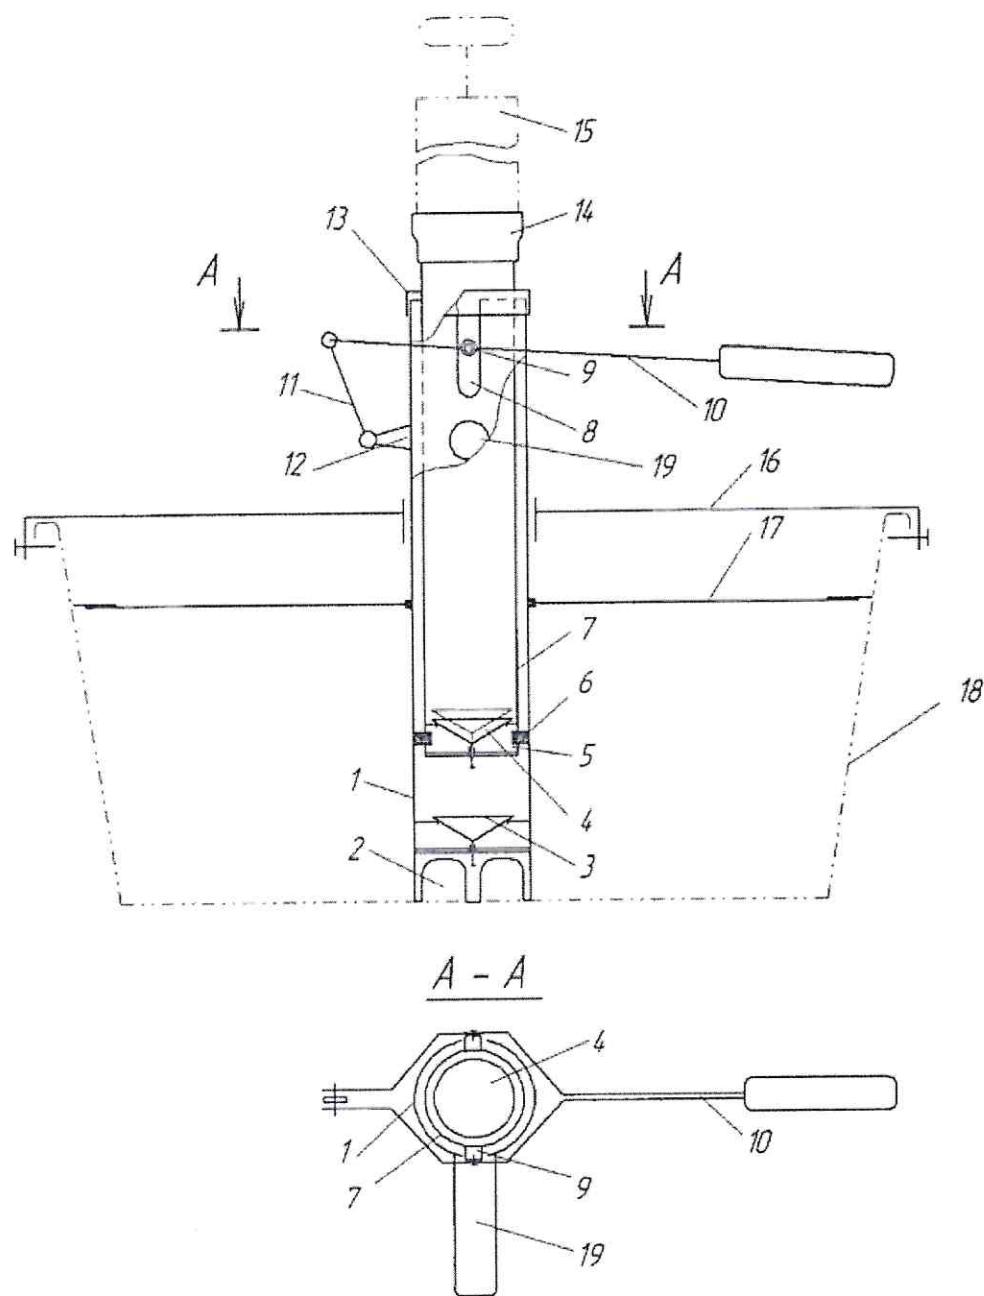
Устройство для подачи консистентной смазки.
